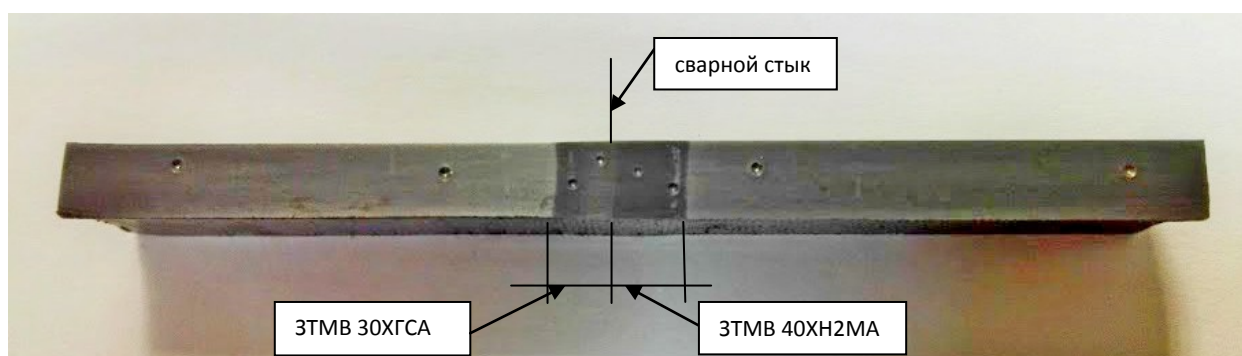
Макроструктура сварного соединения сталей 30ХГСА-40ХН2МА после сварки трением
